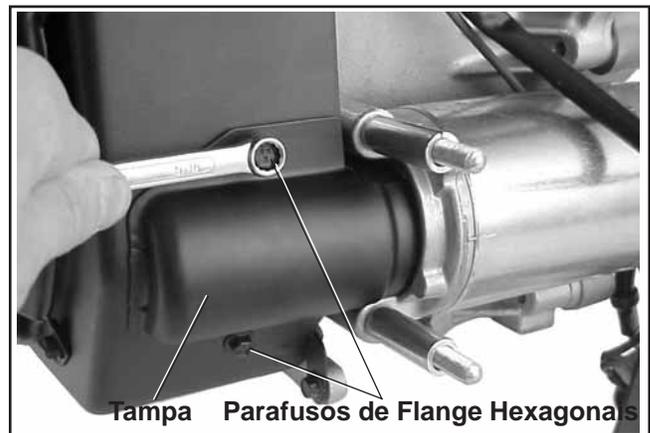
Retirar a Tampa do Motor de Arranque (cremalheira).
